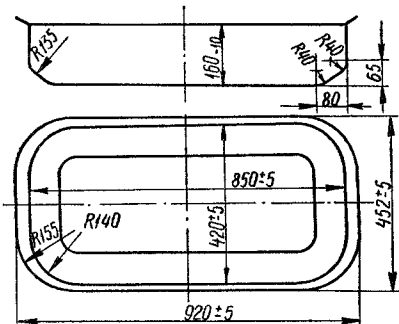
Размеры и форма заготовки для цельноштампованного корыта
